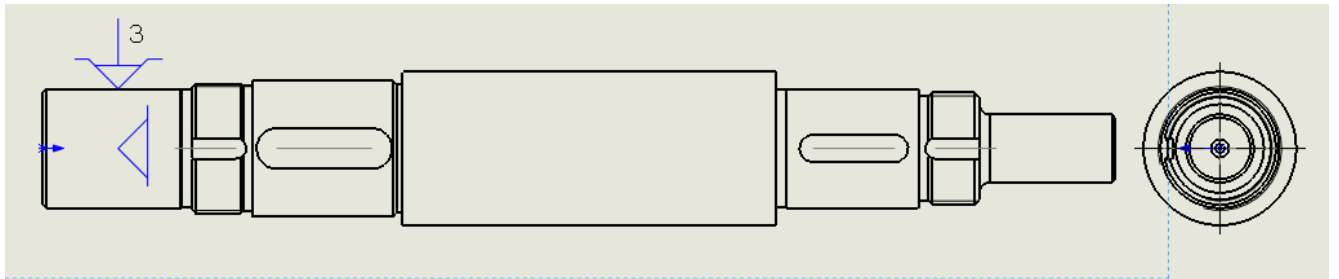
Теоретична схема базування обробки поверхонь 1 – 2.
